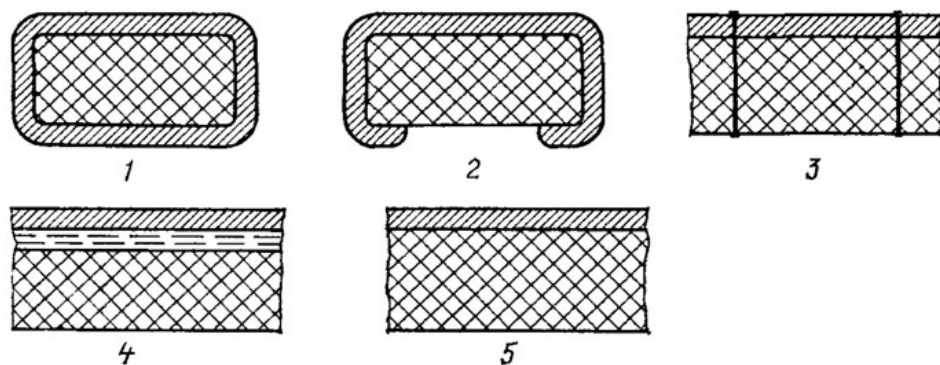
Механические способы крепления металлического покрытия к пластмассе: 1 - обволакивание, 2 - огибание, 3 - заклепывание, 4 - склеивание, 5 - горячее тиснение или заливка (сварка).
